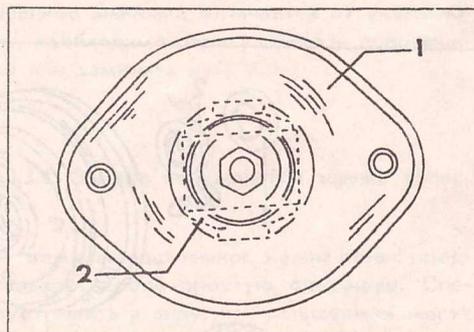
Перед затяжкой гайки штока амортизатора установить верхнюю опору стойки так, как показано на рисунке. 1 опора амортизаторной стойки 2 нижняя втулка
